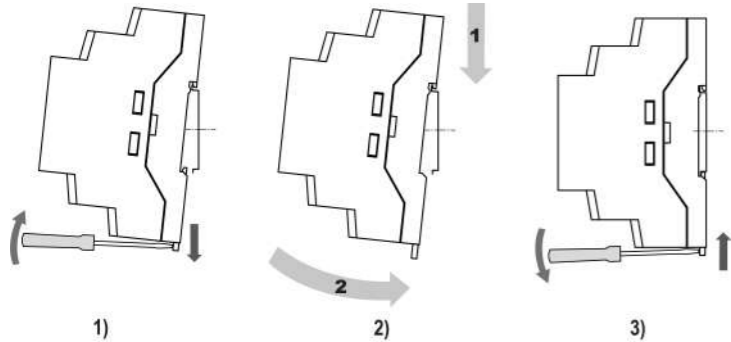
Монтаж прибора с креплением на DIN-рейку
